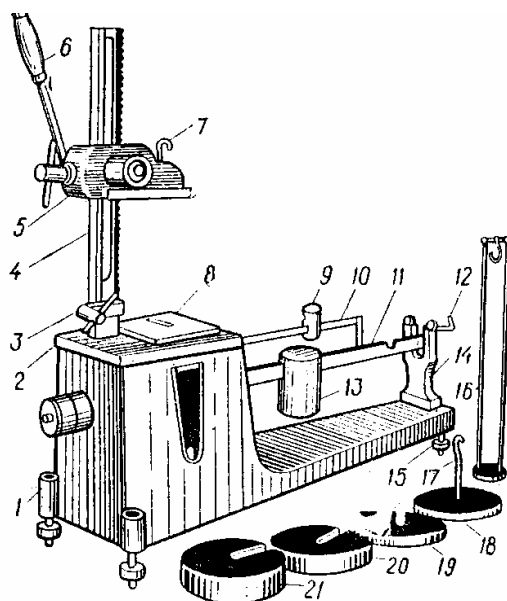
Пристрій для перевірки довжини пружин і пружності пружин та поршневих кілець:
